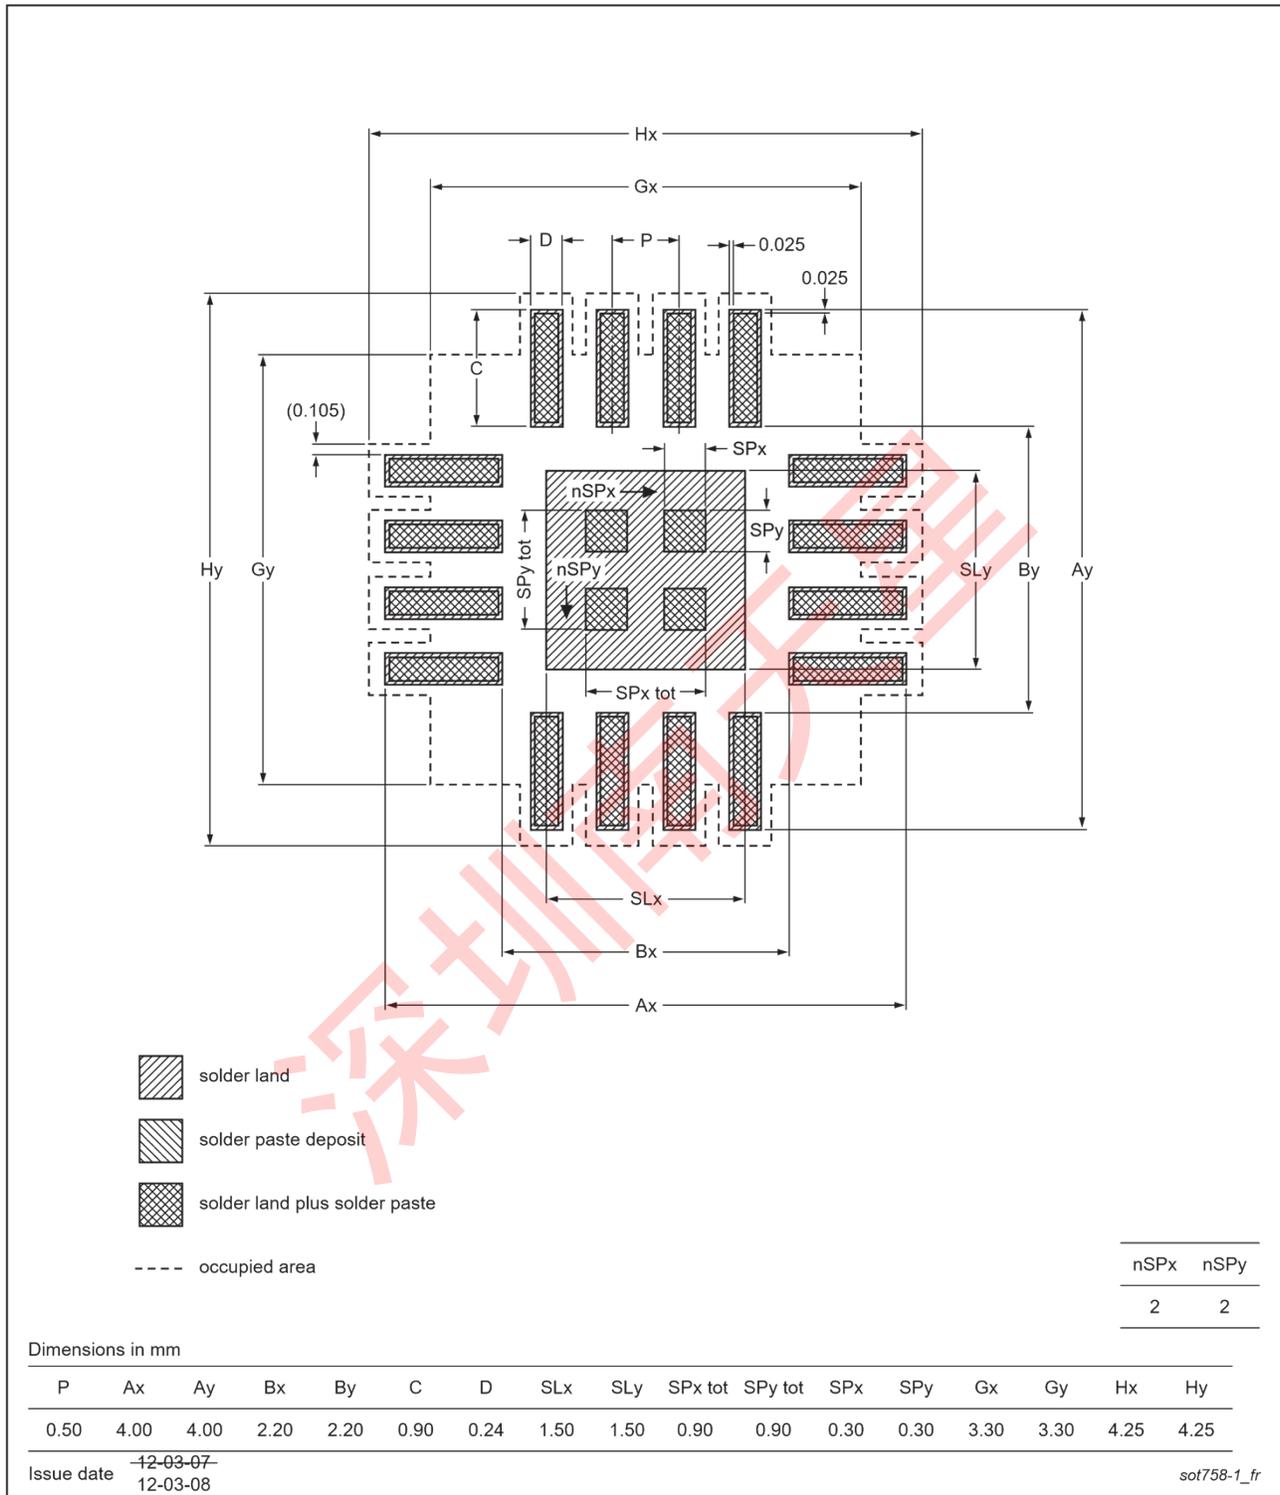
SOT758-1 (HVQFN16) 的 PCB 占地面积; 回流 soldering
